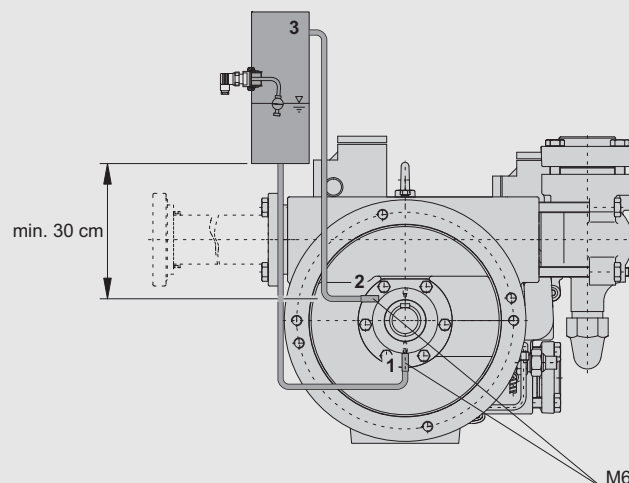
Behälter für Ölvorrat an Wellenabdichtung anschließen
